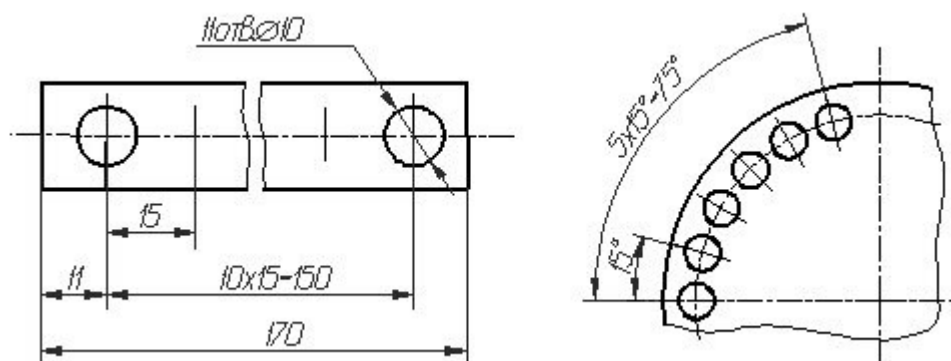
Примеры нанесения размеров равномерно расположенными
